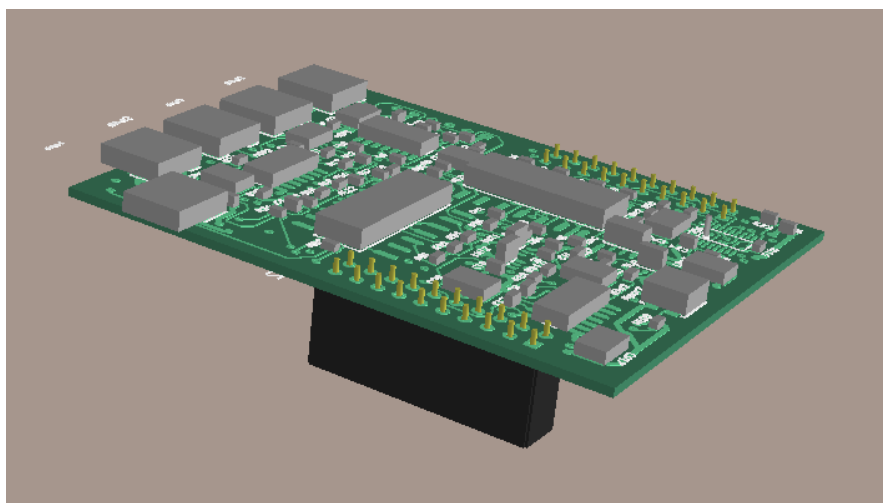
27 Vista isométrica inversa de la placa desarrollada.
